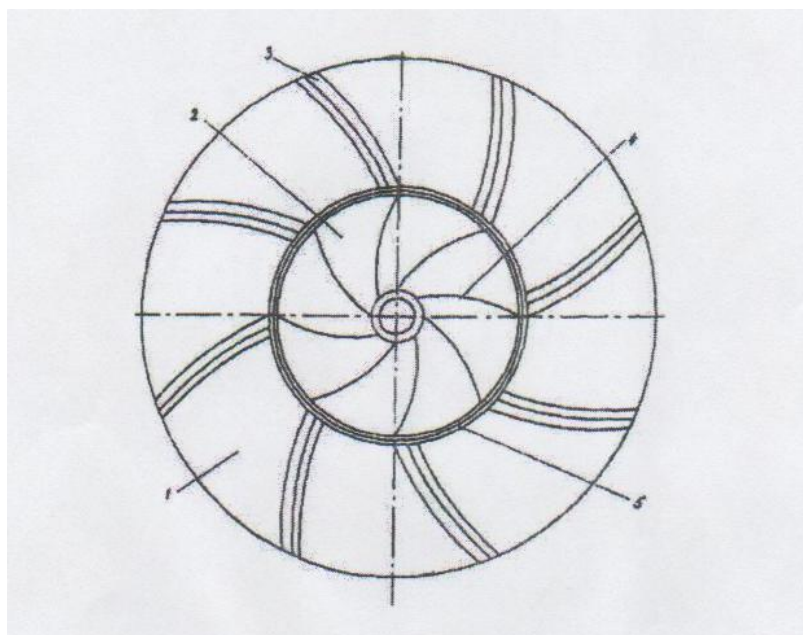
3. Робочий орган відцентрового розкидача (вид зверху): 1 - конусний диск; 2 — псевдосфера; 3,4- лопатки; 5 - циліндричний стакан.
